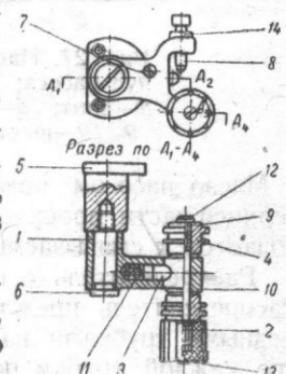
Картетка барабана мальтийского креста: 1—кронштейн с осью; 2—головка; 3—фиксатор; 4—ролик; 5—фланец; 6, 7 и 8—винты; 9, 10—шайбы; 11—пружина; 12, 13—винты, 14—гайка
